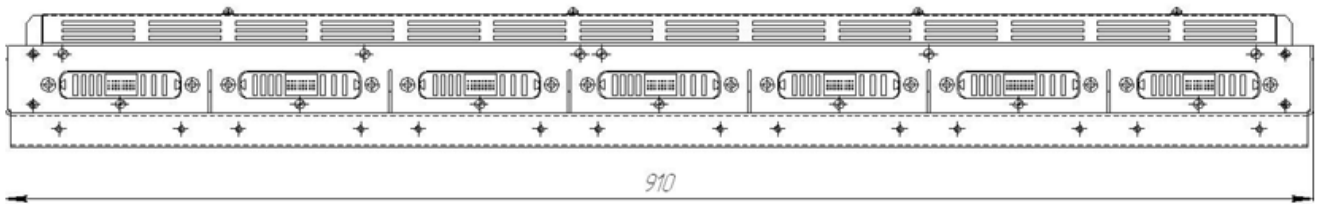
Внешний вид и габаритные размеры кассеты ЗПУ-10-4 с установленными модулями питания ЗПУ-10П-220 (ЗПУ-10П-110)
